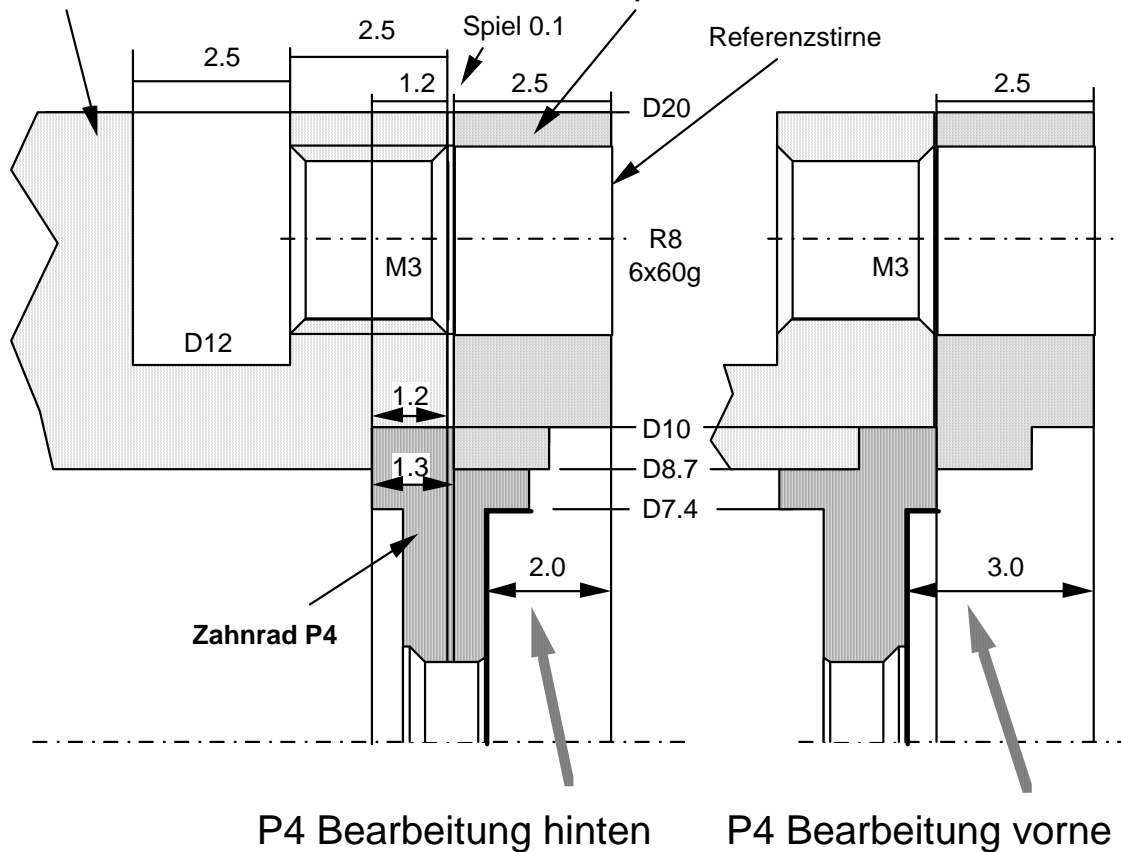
Detail Zahnrad und Hilfswerkzeuge
